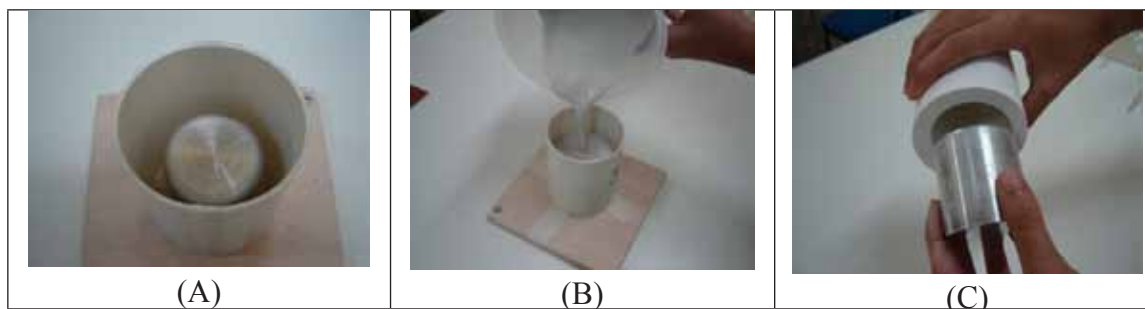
Etapas para fabricação do molde: (A) – Posicionamento da matriz; (B) – Vazamento do gesso e (C) – Remoção da matriz.
